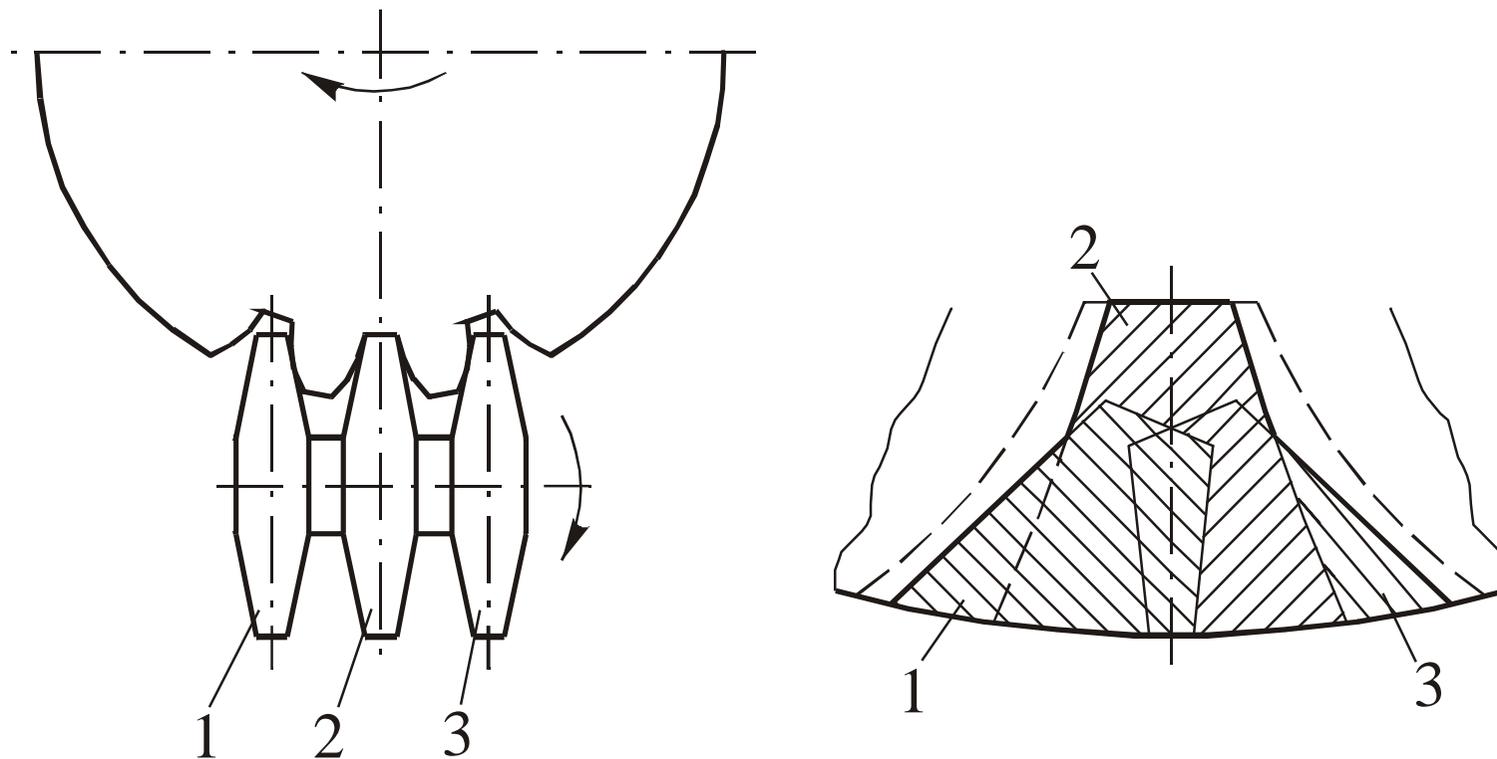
Набор из трех дисковых фрез для чернового нарезания зубчатых колес
